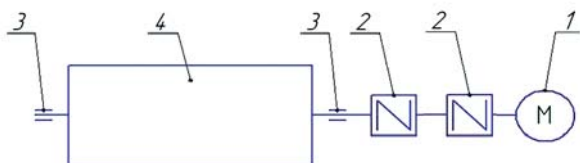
Кинематическая схема привода шаровой мельницы после реинжиниринга: 1 – мотор-редуктор; 2 – муфты зубчатые; 3 – подшипниковые узлы; 4 – мельница
